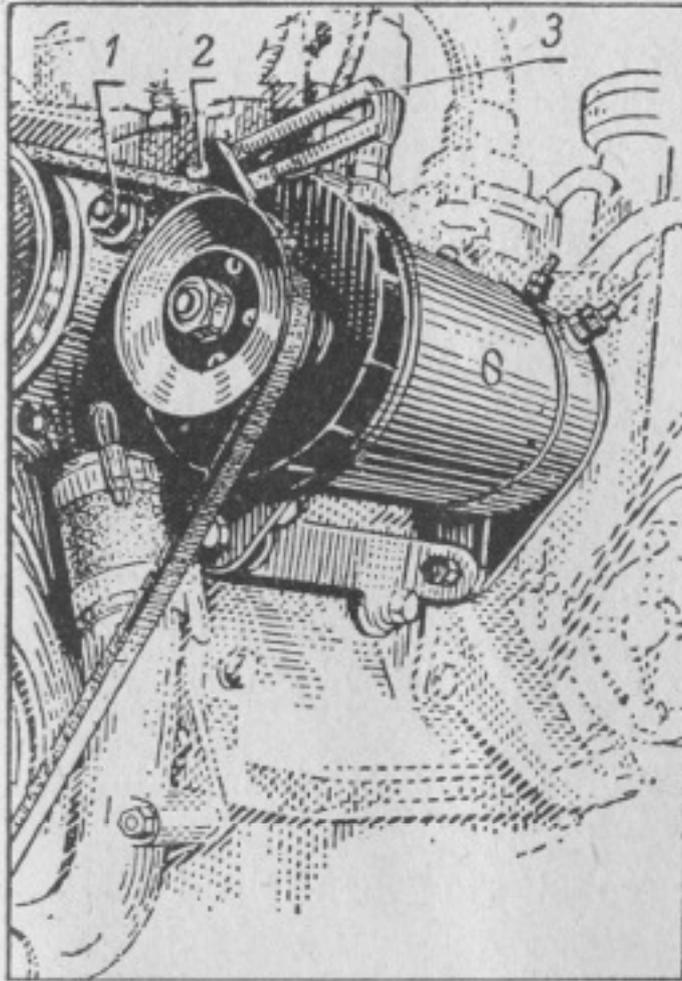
Anordnung und Befestigung der Lichtmaschine am Motor
